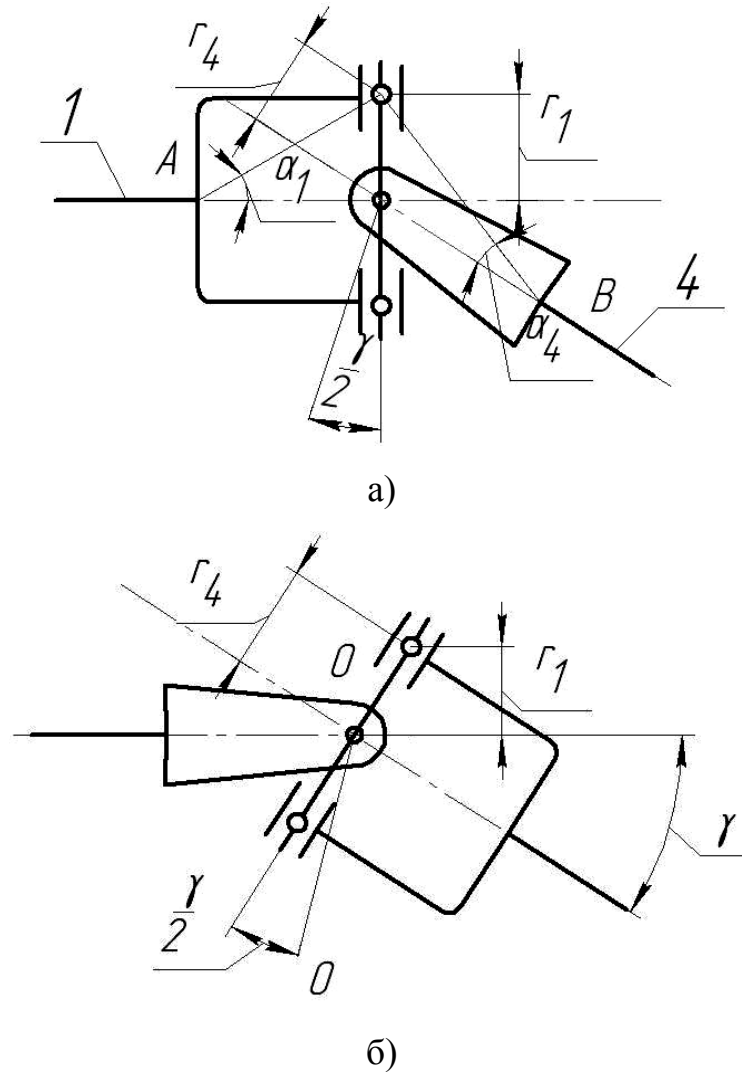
Схема положения вилок и крестовины при повороте ведущего вала на пол-оборота
